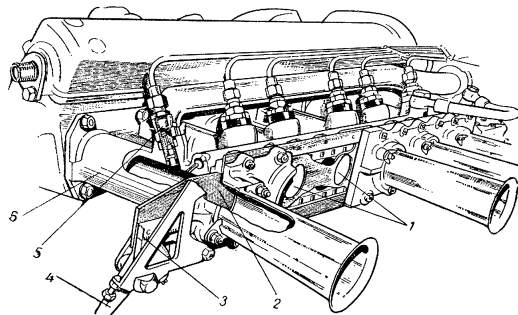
Установка форсунок для впрыска топлива на двигателе автомобиля «Ягуар»:
